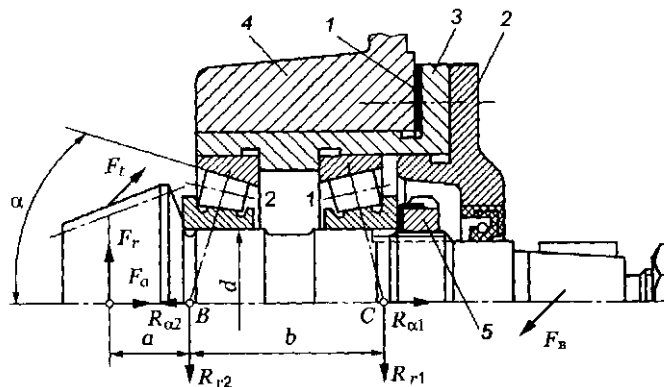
Вал-шестерня конического редуктора. Нагрузка на валу-шестерне: 1 — набор прокладок; 2 — крышка сквозная с манжетой; 3 — стакан; 4 — корпус; 5 — регулировочная гайка
